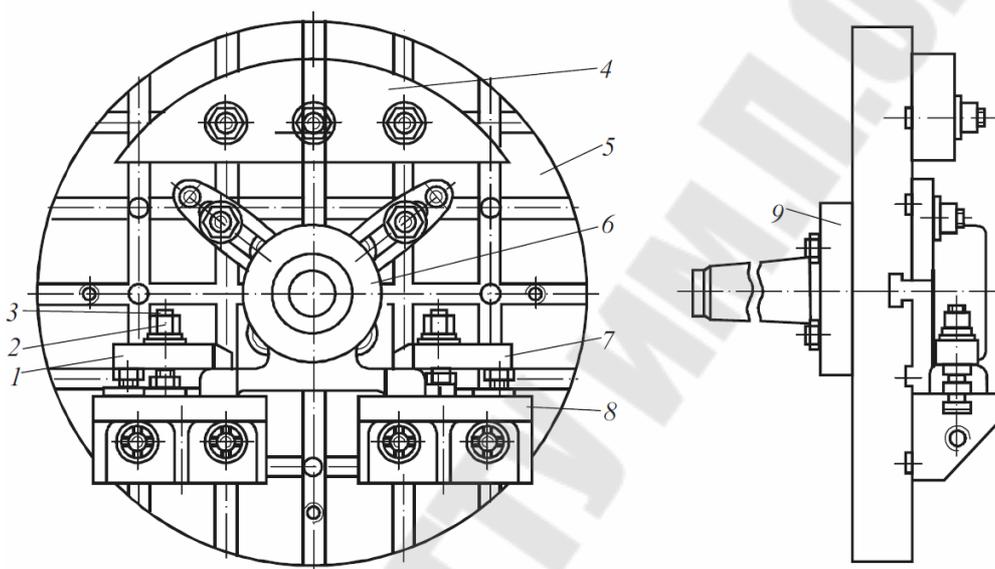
Универсально-сборное приспособление для растачивания отверстия в корпусе подшипника [4]
